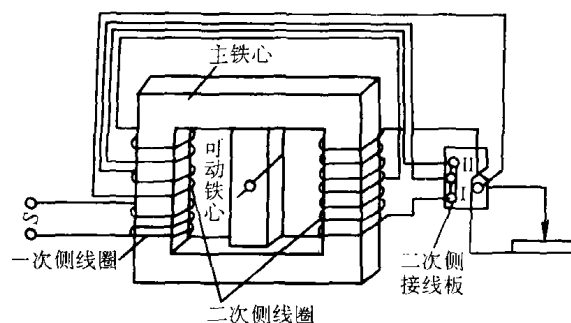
BX1—330 型弧焊变压器的结构原理图
